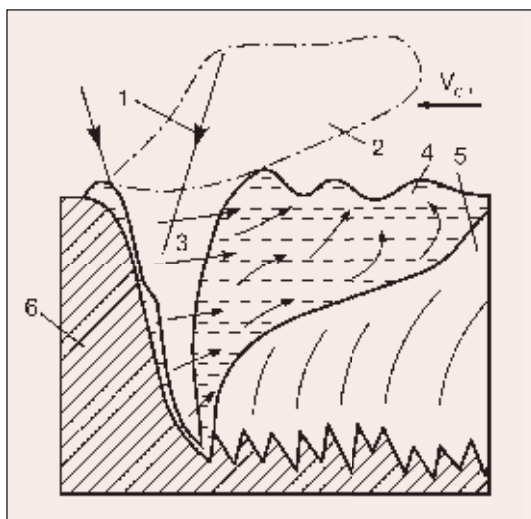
Схема продольного сечения сварочной ванны: 1 — лазерное излучение; 2 — плазменный факел; 3 — парогазовый канал; 4 — хвостовая часть сварочной ванны; 5 — закристаллизовавшийся металл; 6 — свариваемый материал
